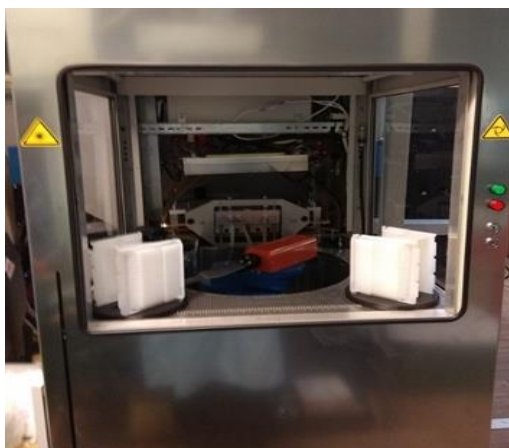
Роботизированная установка быстрой термической обработки кремниевых пластин
